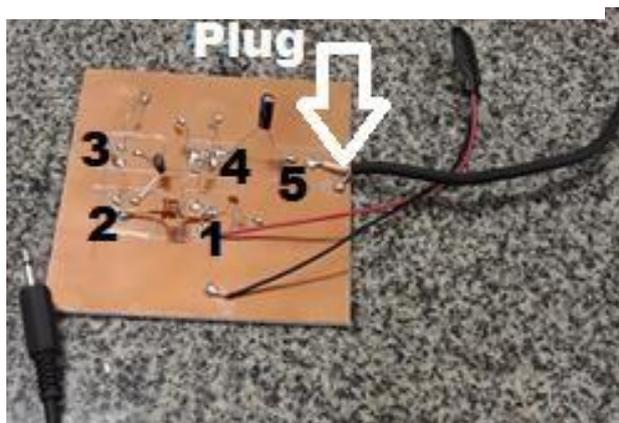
Soldagem do capacitor cerâmico de 10pF e da bobina
